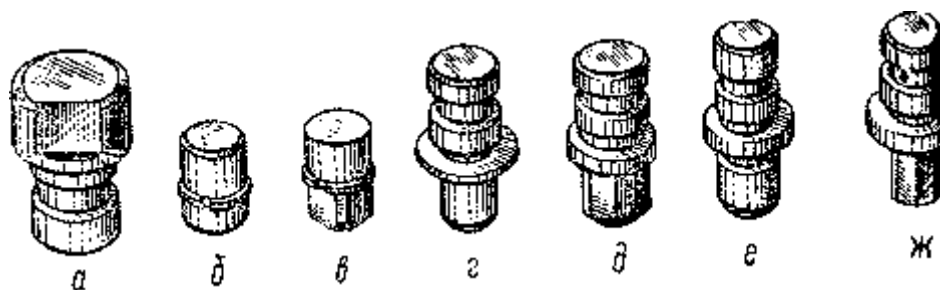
Основные установочные детали для базирования заготовок в приспособлениях, фиксации опорных планок на плитах и угольниках взаимного базирования плит и базирования приспособлений на столах станков: а - шпонки; б - пальцы цилиндрические, в - ромбические, г, е - цилиндрические переходные, д, ж - ромбические переходные.
